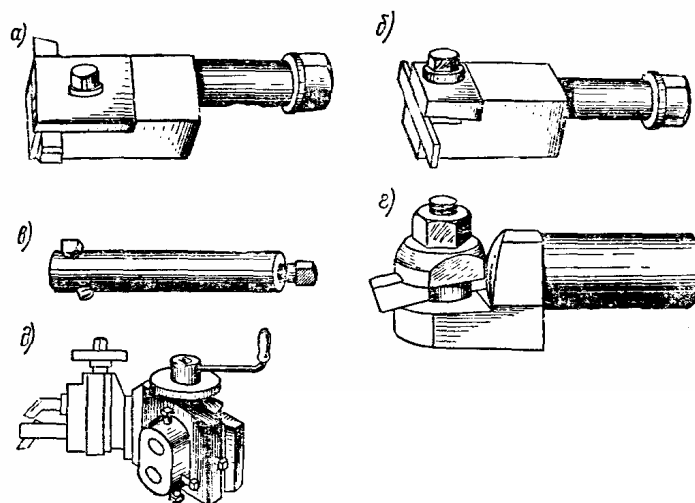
Виды державок к револьверным станкам для крепления резцов:
